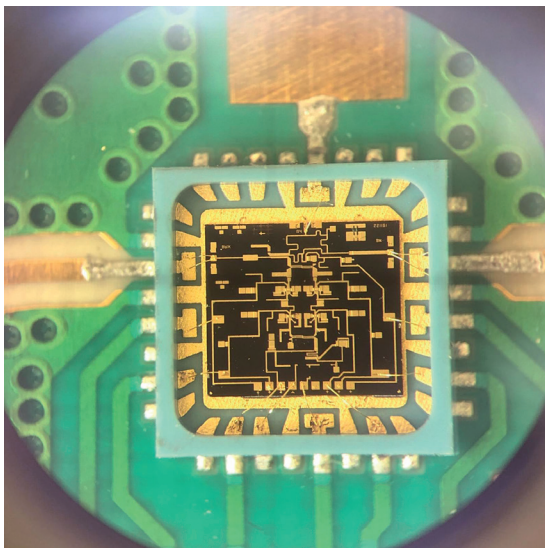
Внешний вид монтажа кристалла МИС ППМ в металлокерамический корпус МК 5169.32-1
